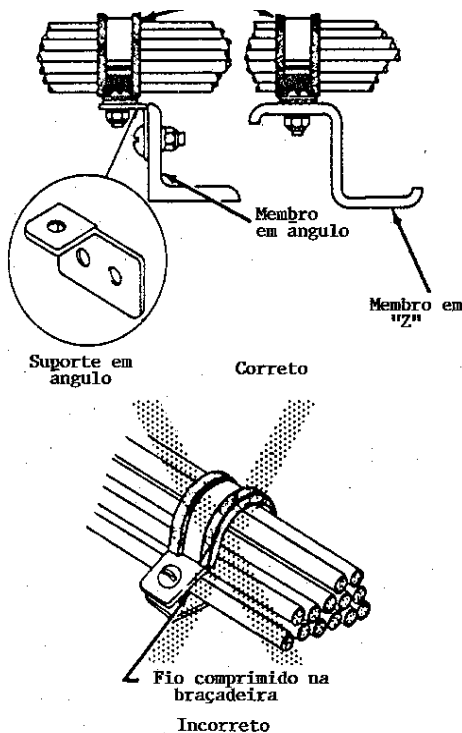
Montagem da braçadeira de cabo na estrutura.
